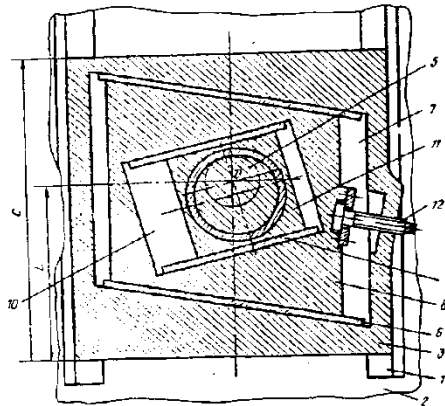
Схема пресса с кулисным механизмом с наклонными направляющими
